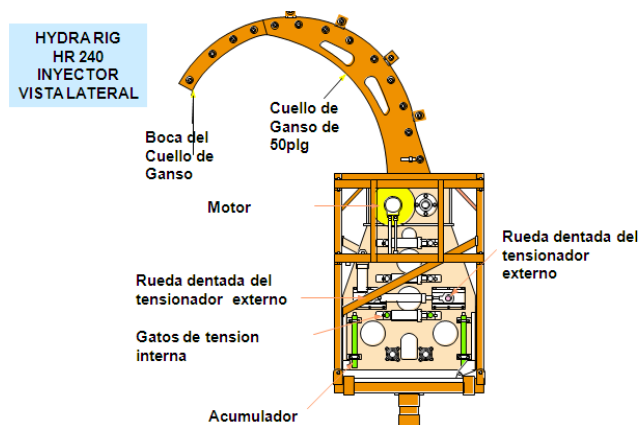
3. Vista frontal de la cabeza inyectora
